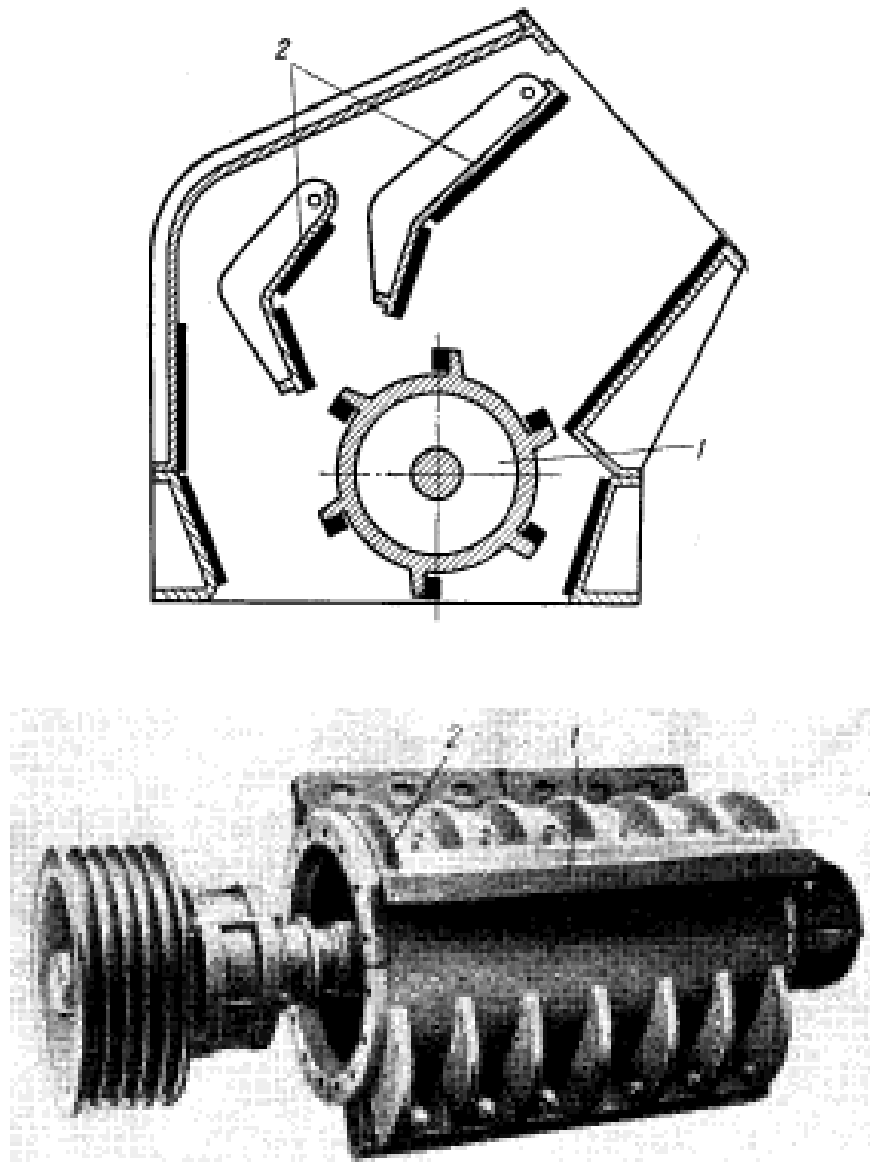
Схема та загальний вигляд ротору роторно-бильної дробарки французької фірми «Дракон»: зверху: 1 – ротор; 2 – відбійні плити; знизу: 1 – било; 2 – корпус ротора
